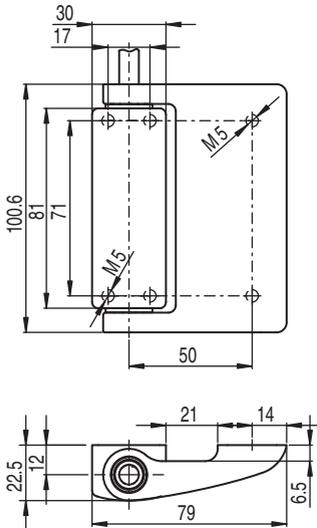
Dimensions du S410-M1CB2-T en mm
